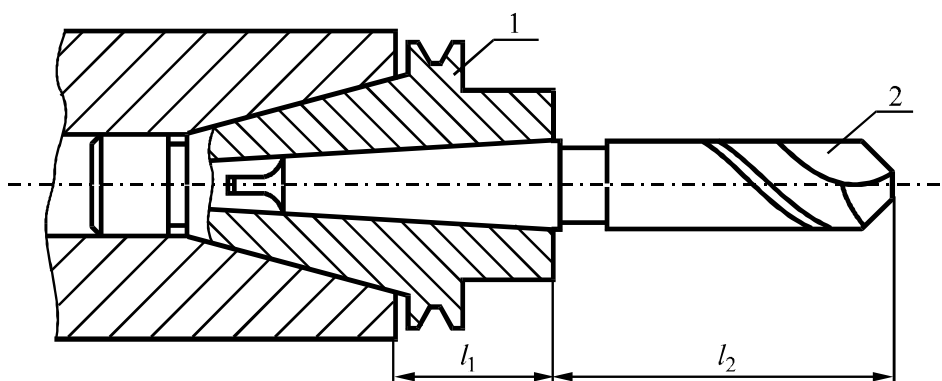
Пример крепления сверла на многоцелевом станке:
